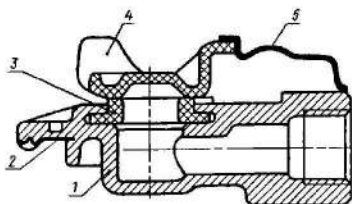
Головка соединительная типа ПАЛМ: 1 — корпус; 2 — вставка; 3 — уплотнитель; 4 — крышка; 5 — фиксатор.
